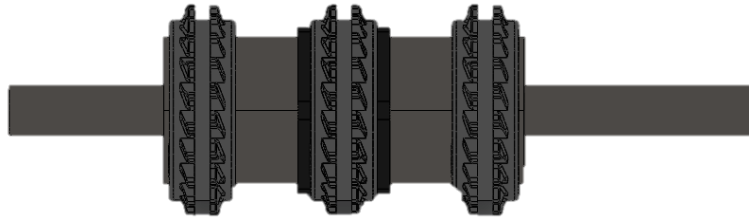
Dibujo CAD que muestra la sujeción de los engranajes al eje motriz.
